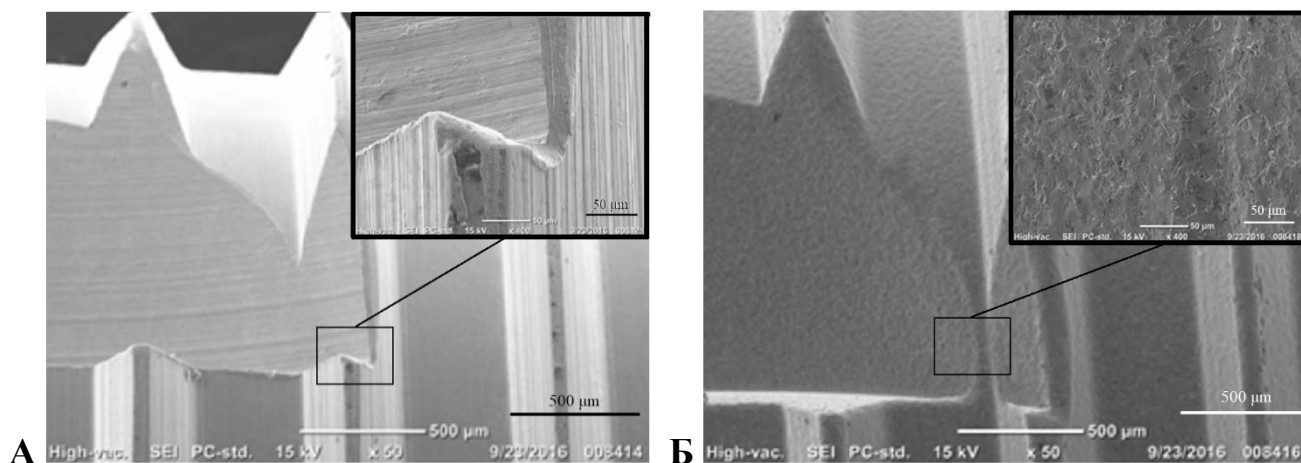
РЭМ-изображения поверхности имплантата: А – фрезерованная поверхность – образец 0; Б – после пескоструйной обработки с различным увеличением – образец М
